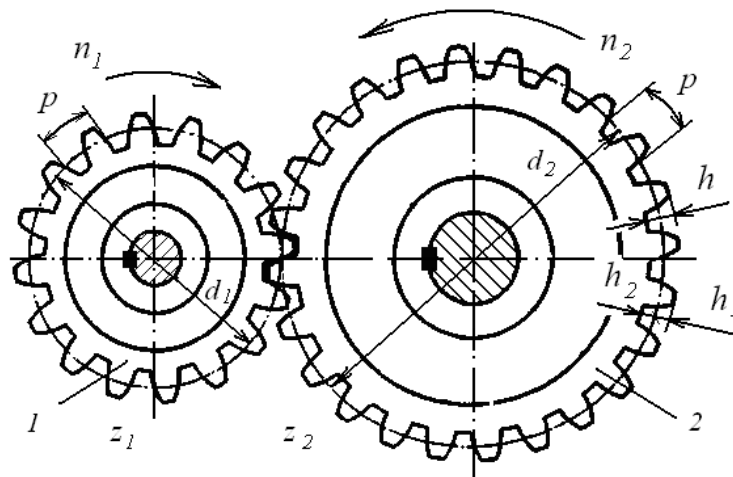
Зубчатая цилиндрическая передача с наружным зацеплением
